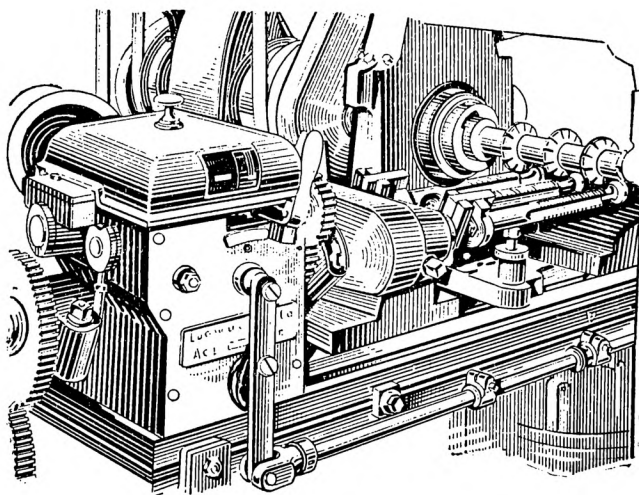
Тройной делительный и фрезерный аппарат с автоматическим механизмом подачи, установленный на универсально-фрезерном станке
